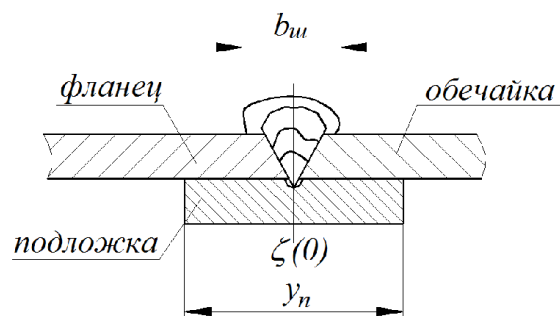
Схема формирования сварного кольцевого шва
